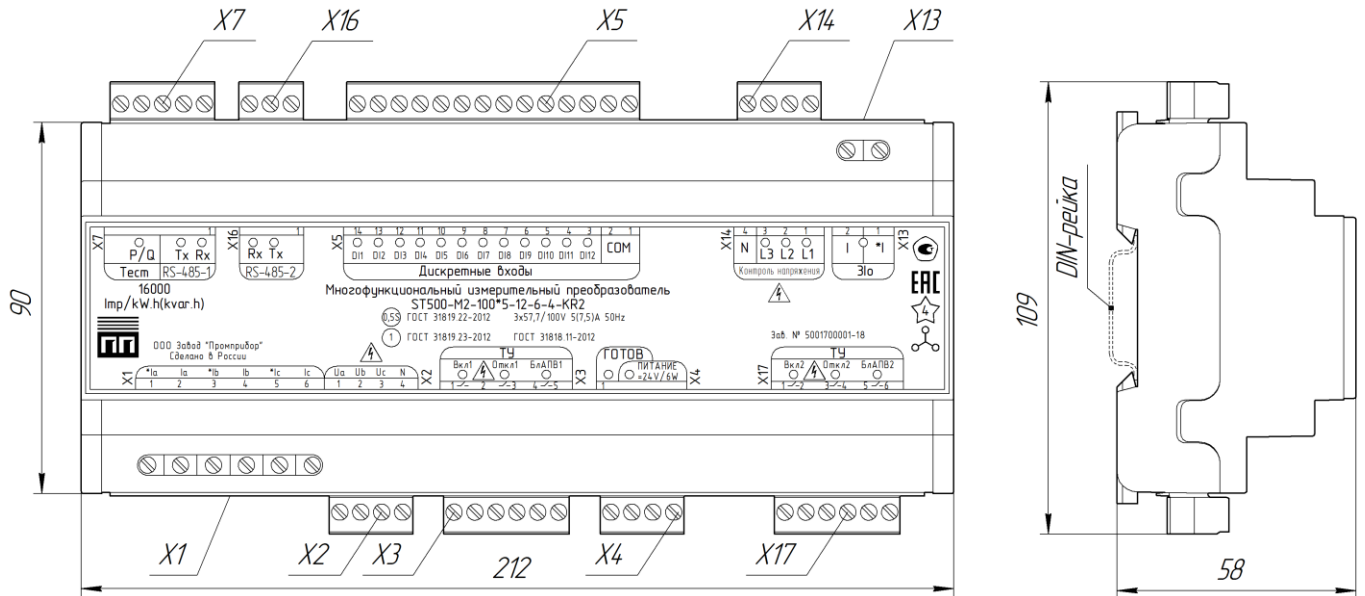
Внешний вид и габаритные размеры МИП
